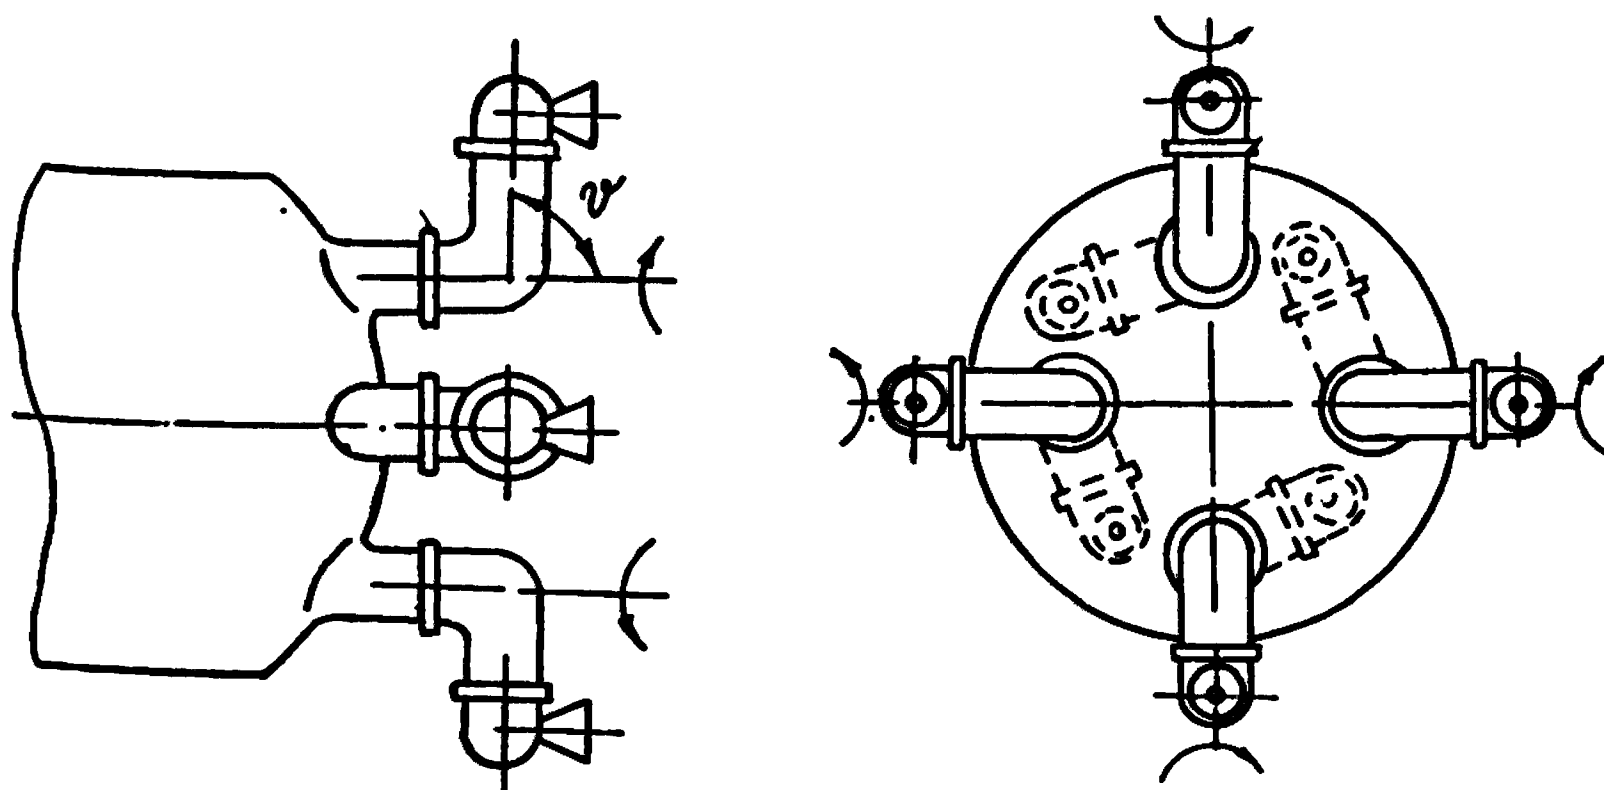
Конструктивная схема исполнительного устройства с четырьмя двухшарнирными ВУС
